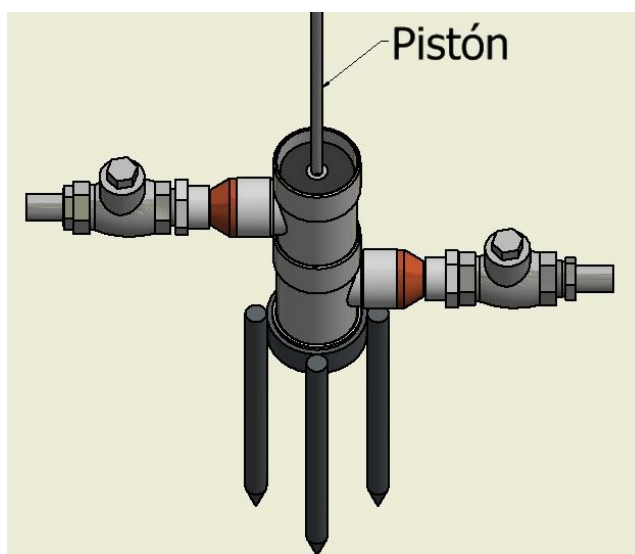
QUINTO PASO DE LA CONSTRUCCIÓN DE LA BOMBA
